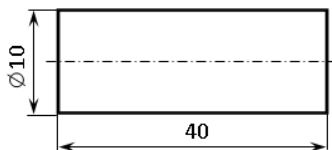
Эскиз детали «вал» с номинальными размерами
